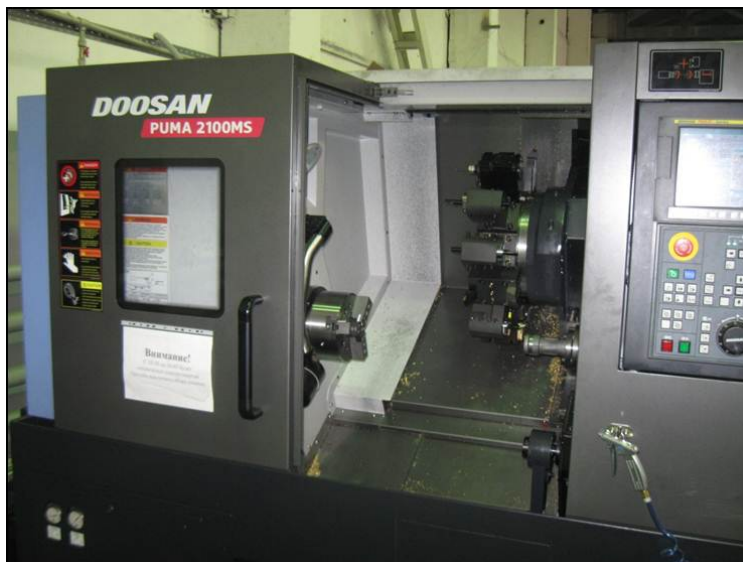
Высокпроизводительный двухшпиндельный токарный обрабатывающий центр PUMA 2100MS с приводным фрезерным инструментом и контр-шпинделем (“DOOSAN”)
